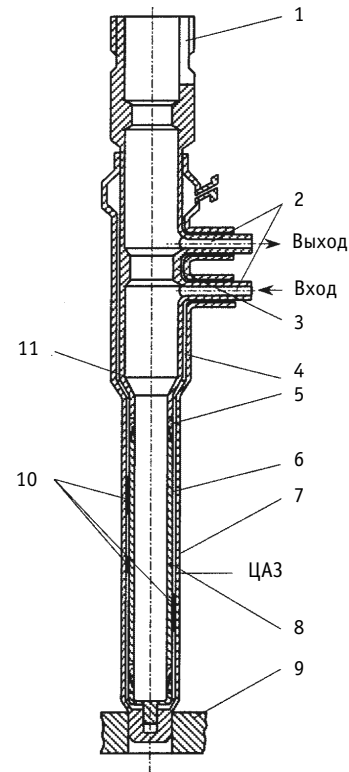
Общий вид канала: 1 – головка канала; 2 – патрубок циркуляционный; 3 – место уплотнения подвески; 4 – вакуумная полость; 5 – переходник сталь-цирконий; 6 – труба циркониевая; 7 – корпус защитный; 8 – датчик температуры; 9 – нижняя плита реактора; 10 – датчик нейтронного потока; 11 – корпус (ЦАЗ – центр активной зоны)
